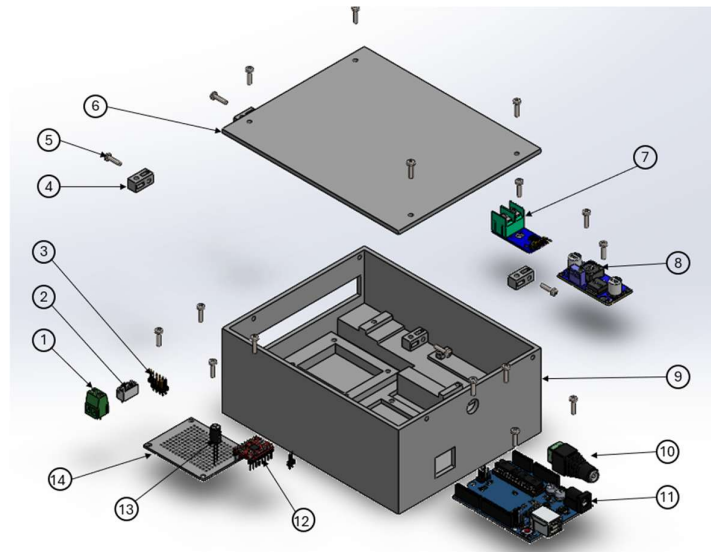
Vista isométrica explosionada de la caja electrónica
